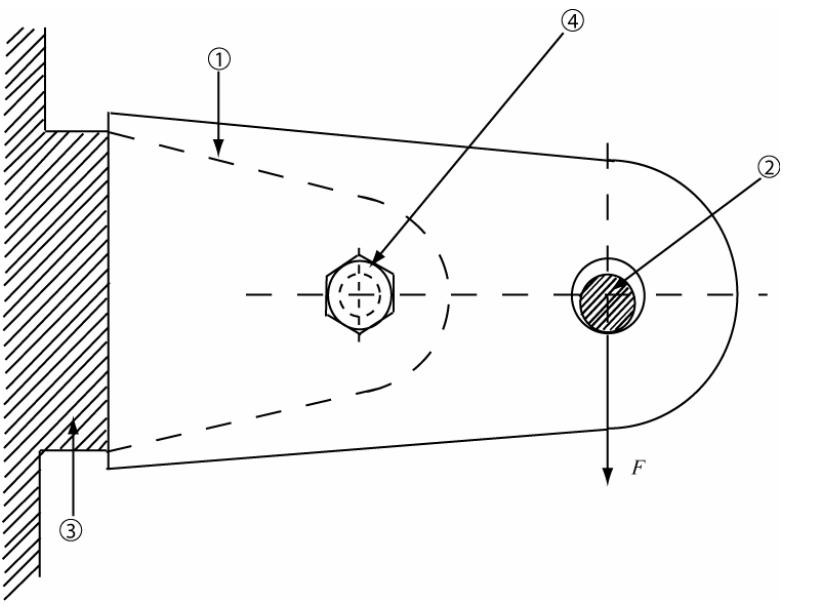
Selle pour poteau – essai de flexion5.5.2.6.2 Essais supplémentaires pour selles pour poteau
